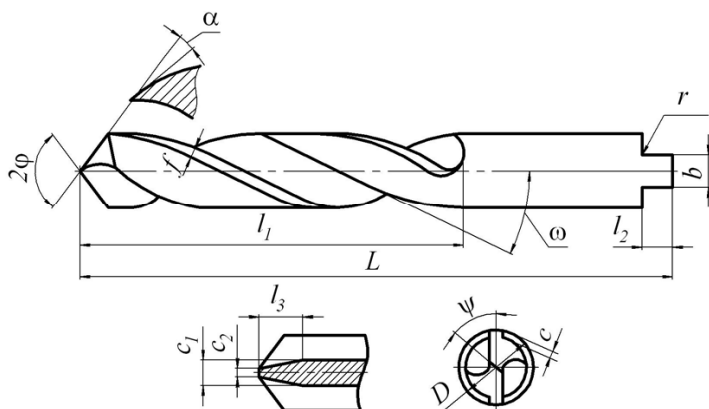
Типовая конструкция сверла с цилиндрическим хвостовиком
